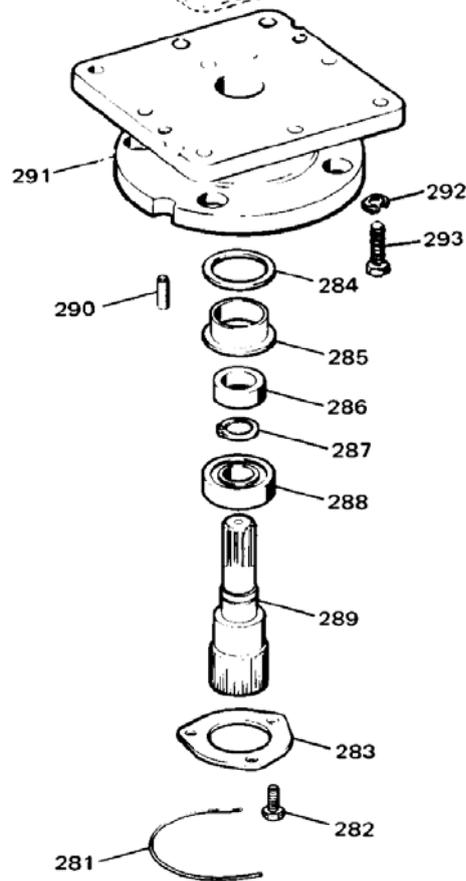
Покомпонентный чертеж стандартной базы PGA в сборе
